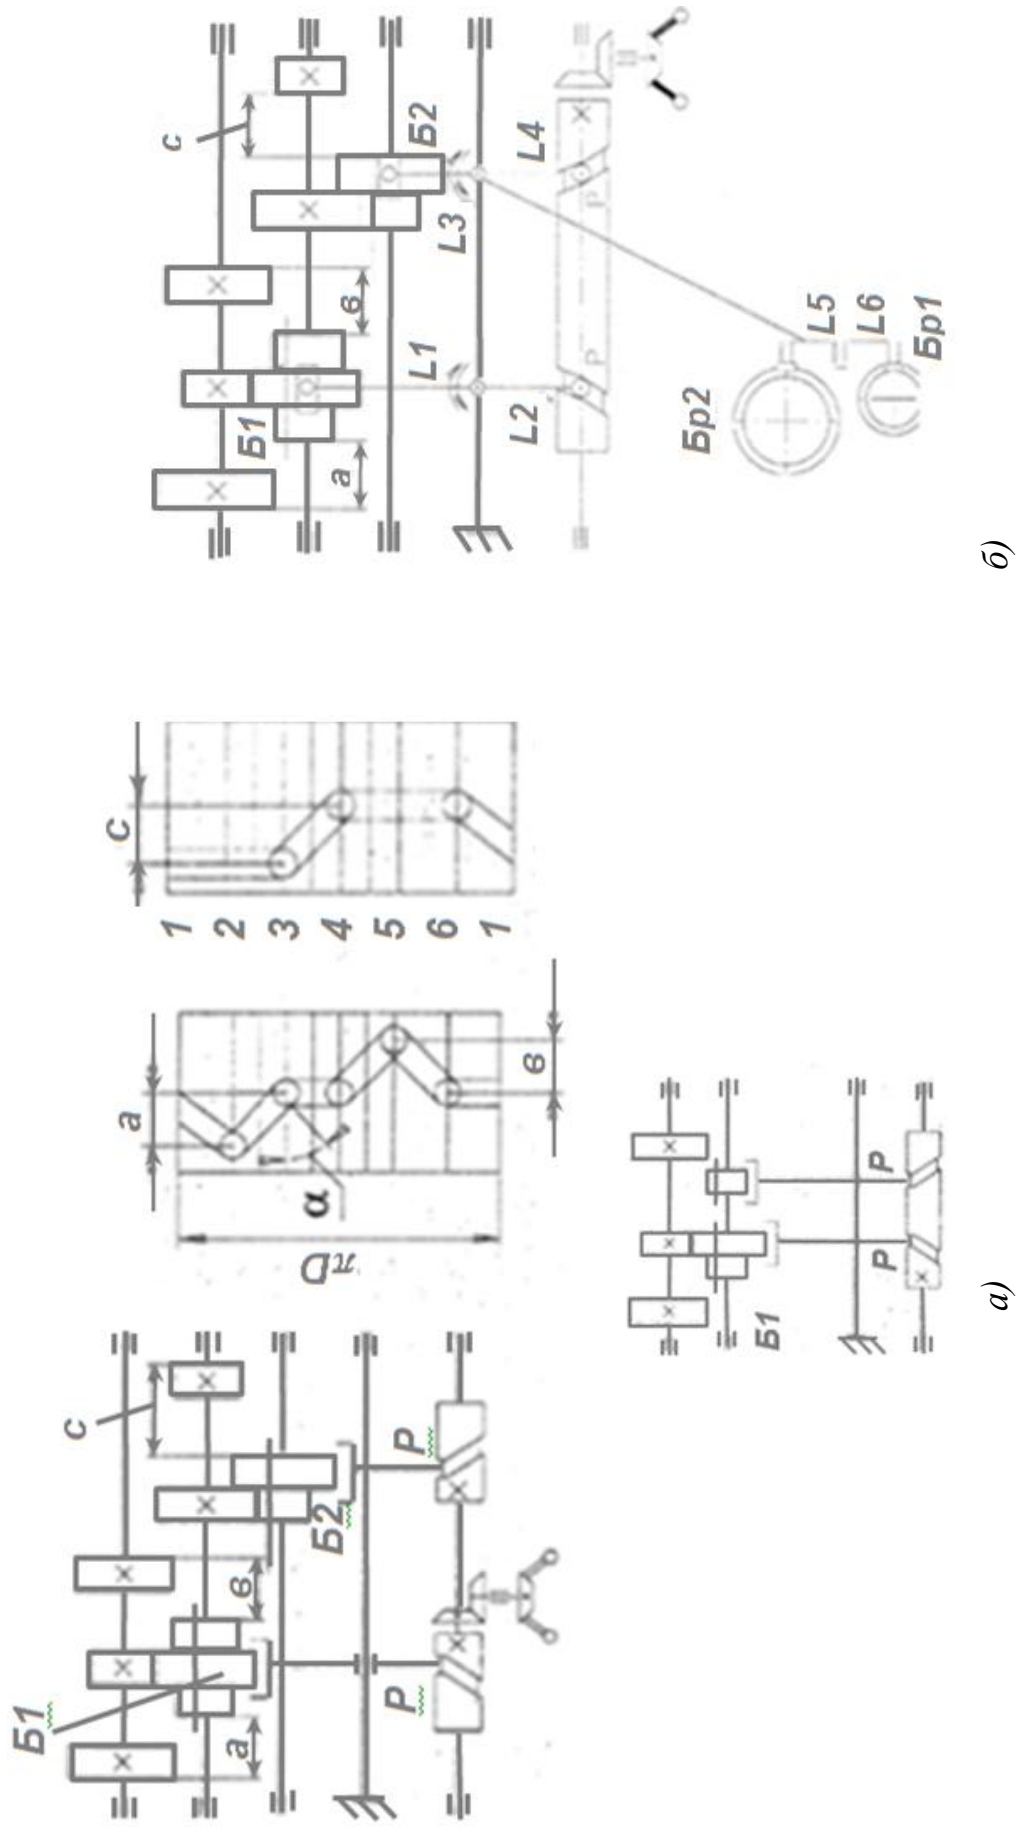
Схемы механизмов для получения прерывистых движений
